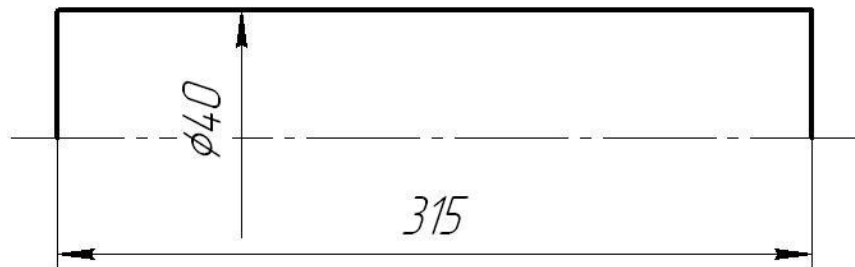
Рисунок заготовки, получаемой прокатом
